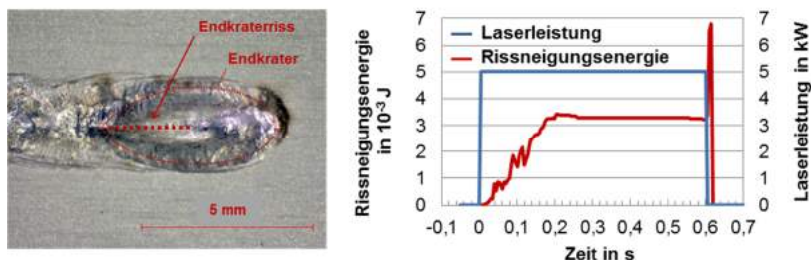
Links: Endkraterriss am Schweißnahtende in der Aufsicht.
